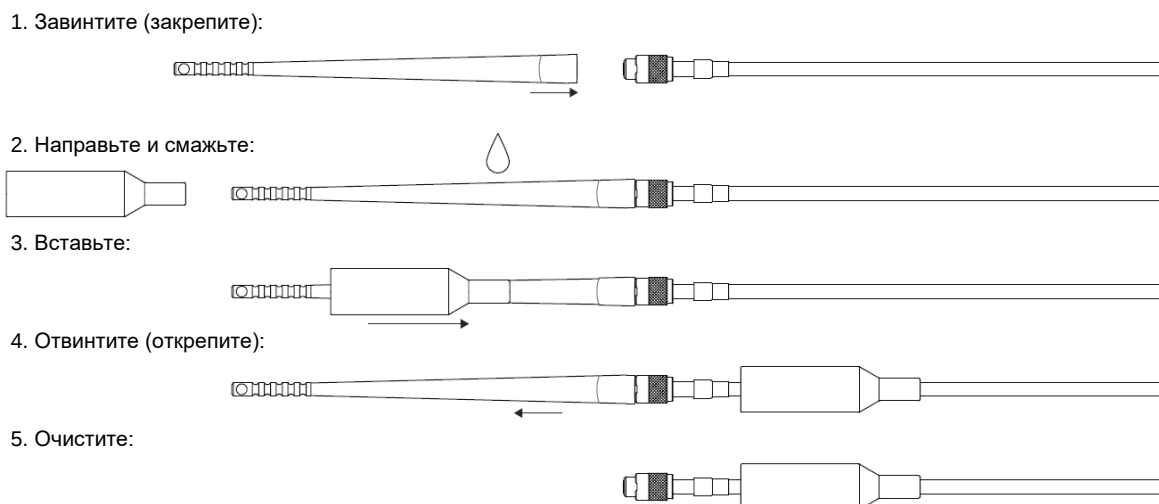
Сборка защиты межсоединений IP172 для удлинительного кабеля EA90x
